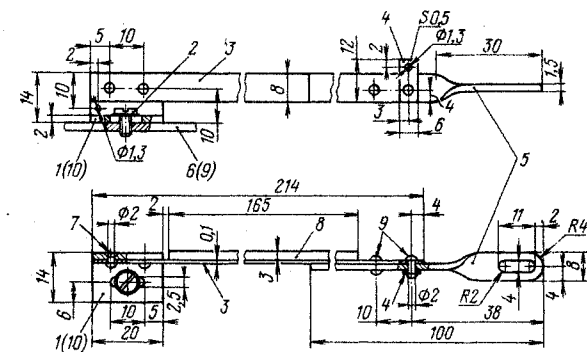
Тормоз подающего узла: 1 — угольник, АМц-П; 2 — винт М2,5×5; 3 — лента тормоза, Ст.65Г; 4 — планка Ст.10кп; 5 — тяга, Ст.10кп; 6 — шасси блока перемотки; 7, 9 — заклепки алюминиевые, по 2 шт.; 8 — накладная, фетр, приклеить к дет. 3 клеем БФ-2
